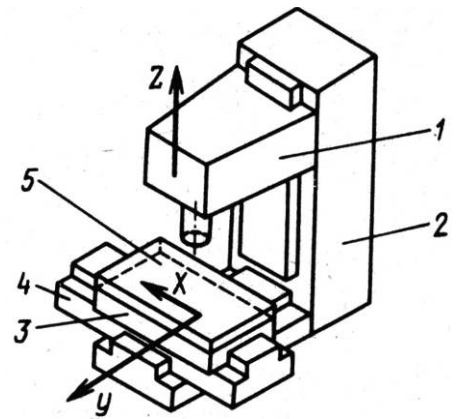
Вертикальный ГПМ для обработки плоских деталей с неподвижной стойкой и крестовым столом
